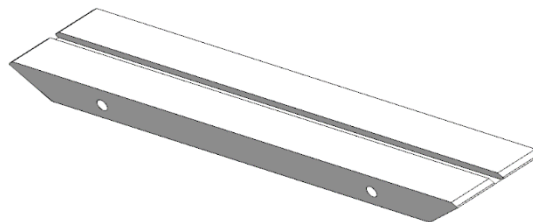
Placa de PE 1000. Módulo del freno separador de correas. Mecanizada.
